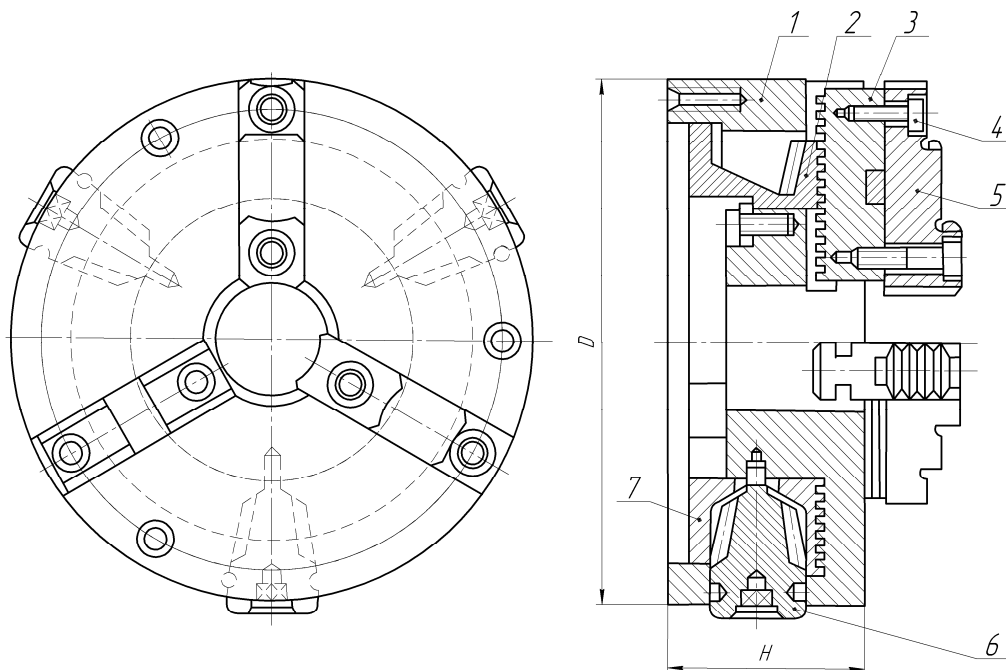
Будова й параметри трикулачкового самоцентрівного патрона: 1 – корпус; 2 – диск; 3 – рейка; 4 – гвинт; 5 – накладний кулачок; 6 – конічне зубчасте колесо; 7 – кришка; *H* – ширина патрона; *D* – діаметр корпусу патрона
